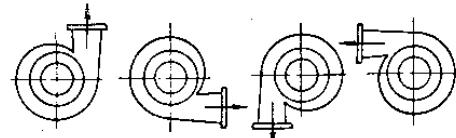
Возможные положения напорного патрубка консольного насоса.
